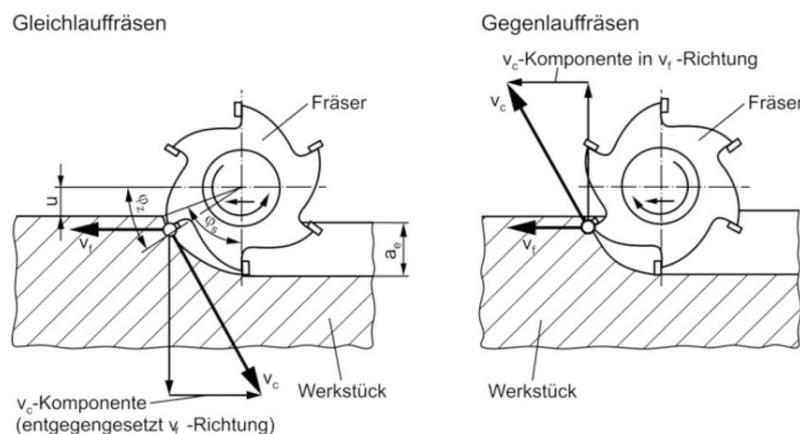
Gleich- und Gegenlaufräsen; Quelle: Werkzeugmaschinen Aufbau, Funktion und Anwendung vonspanenden und abtragenden Werkzeugmaschinen, Springer
